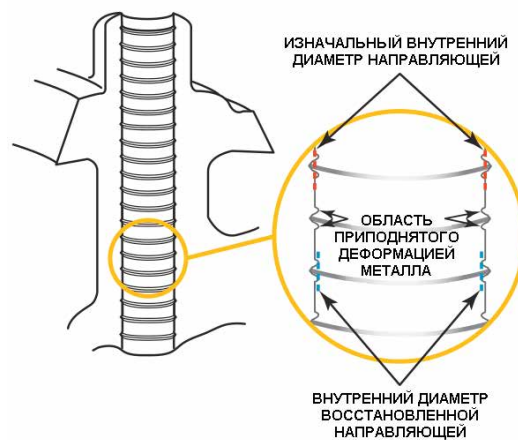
Разрез направляющей клапана с сформированными на внутренней поверхности накаткой желобками и выступами металла; источник: Pearson Education, Inc.
